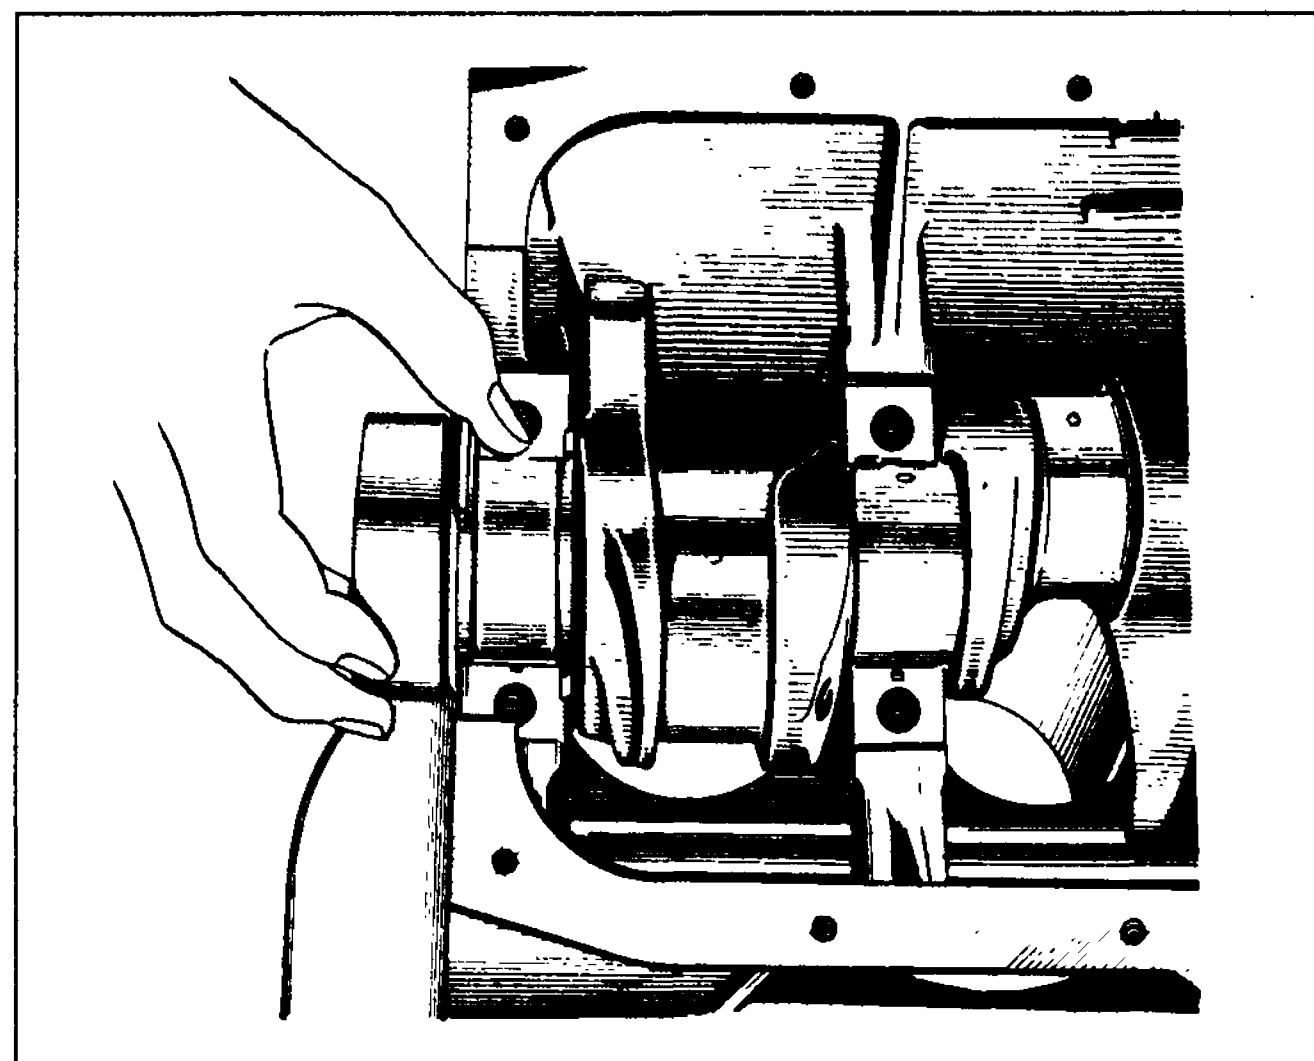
Установка упорных полуколец на задней опоре коленчатого вала
